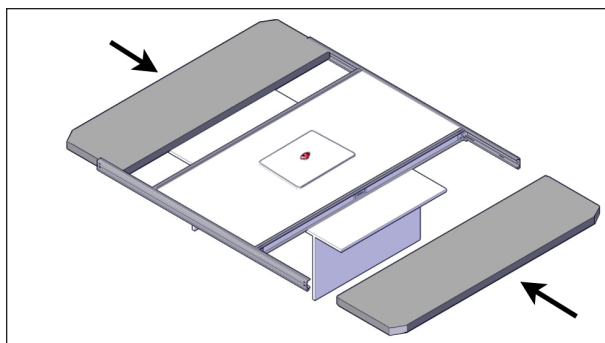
INSTALLATION DES PANNEAUX LATÉRAUX
